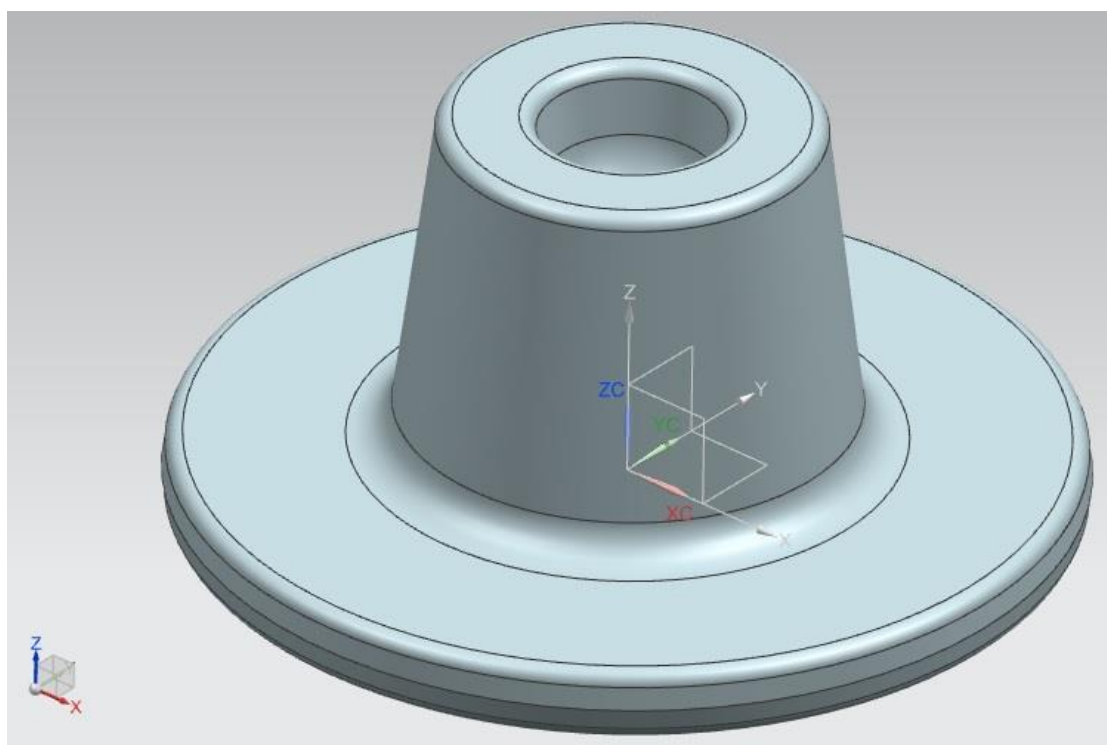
3D-модель гарячої заготовки деталі «Кришка»
